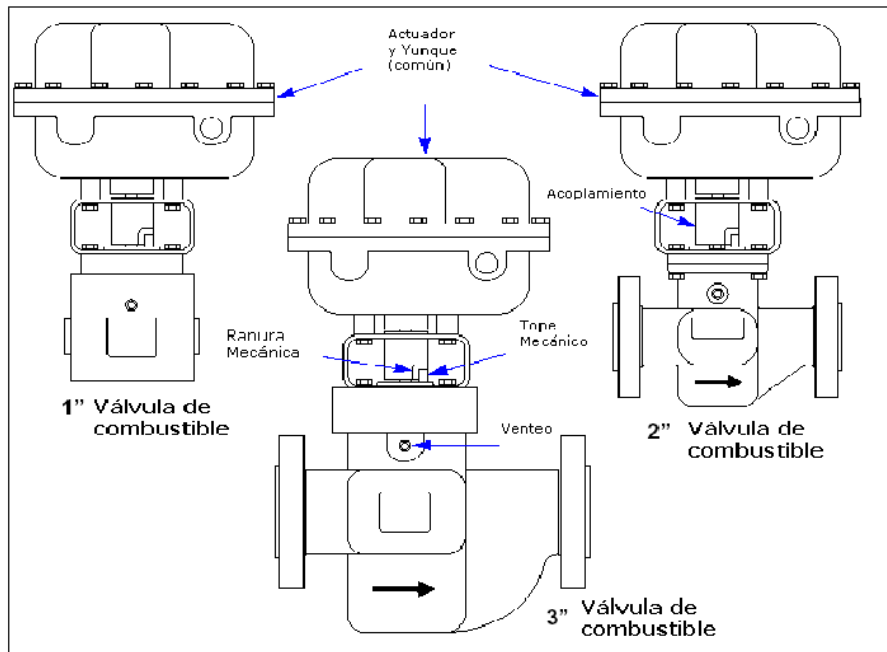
Válvula de combustible (Fuente: Rotary fuel valve and position controller for gas turbines)
